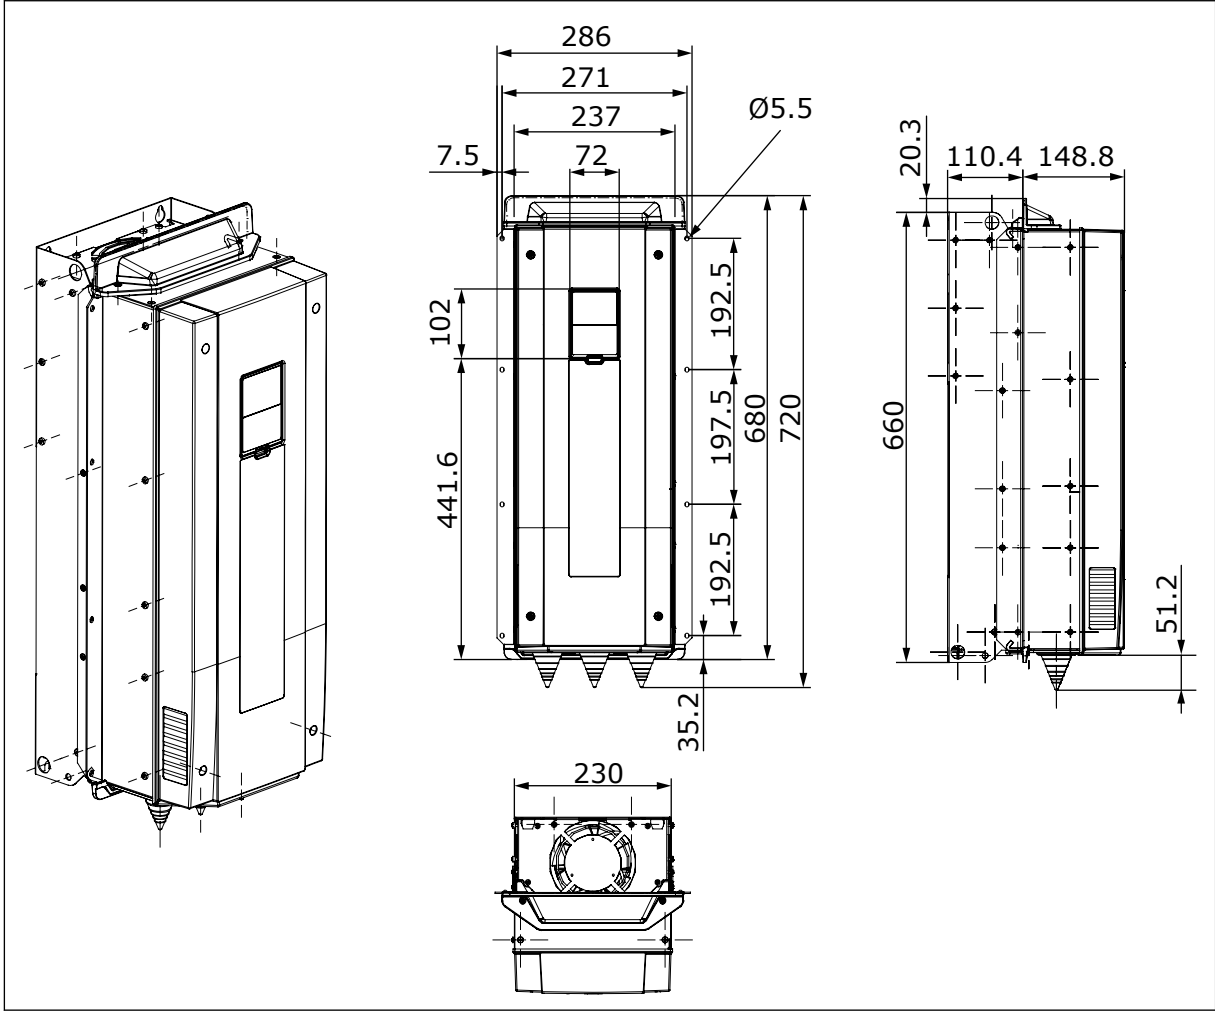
AC sürücünün boyutları, flanş tipi montaj, MR5 [mm]
